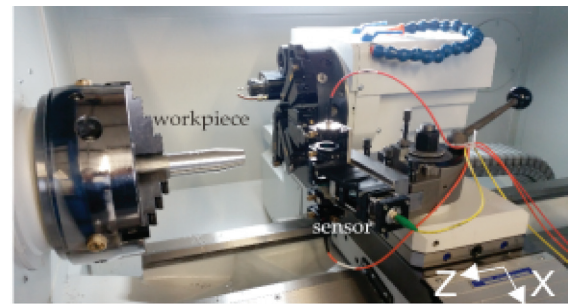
P-LDD Sensor in Werkzeugmaschine. Der Sensor ist gegenüber dem Werkzeugrevolver montiert. Dies ermöglicht eine gleichzeitige Messung und Bearbeitung des Werkstückes [6].
